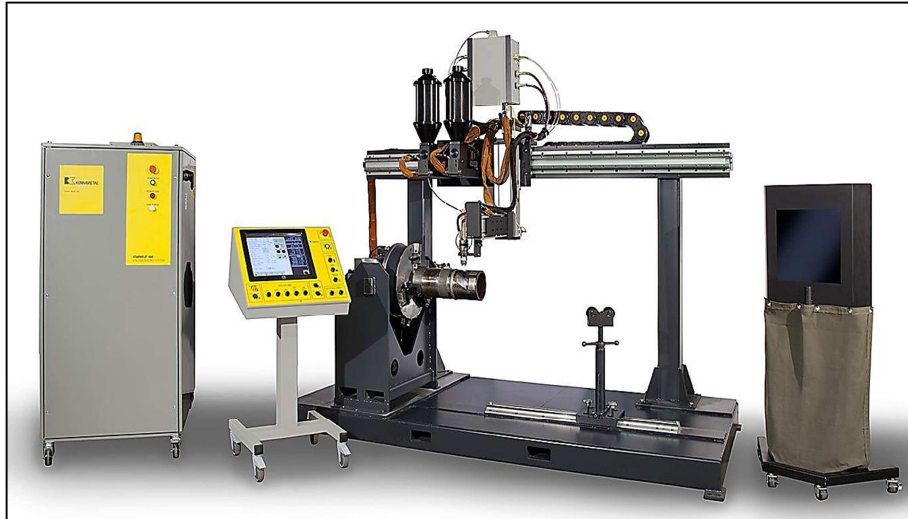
Equipamento mecanizado de soldagem de revestimento plasma pó do fabricante Kennametal (Adaptado de Kennametal, 2016).
